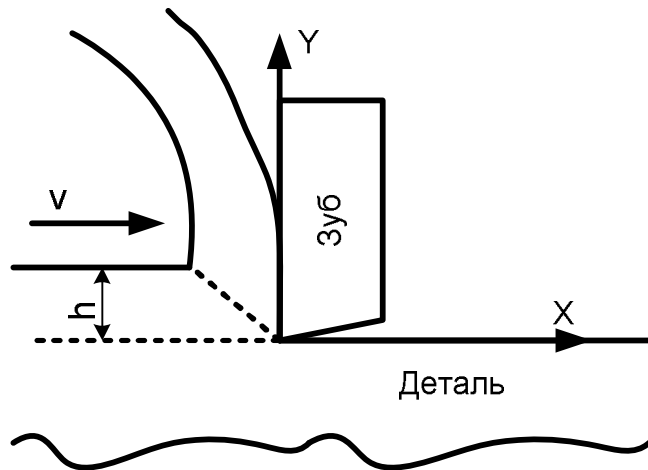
Розрахункова схема напруження зуба фрези
